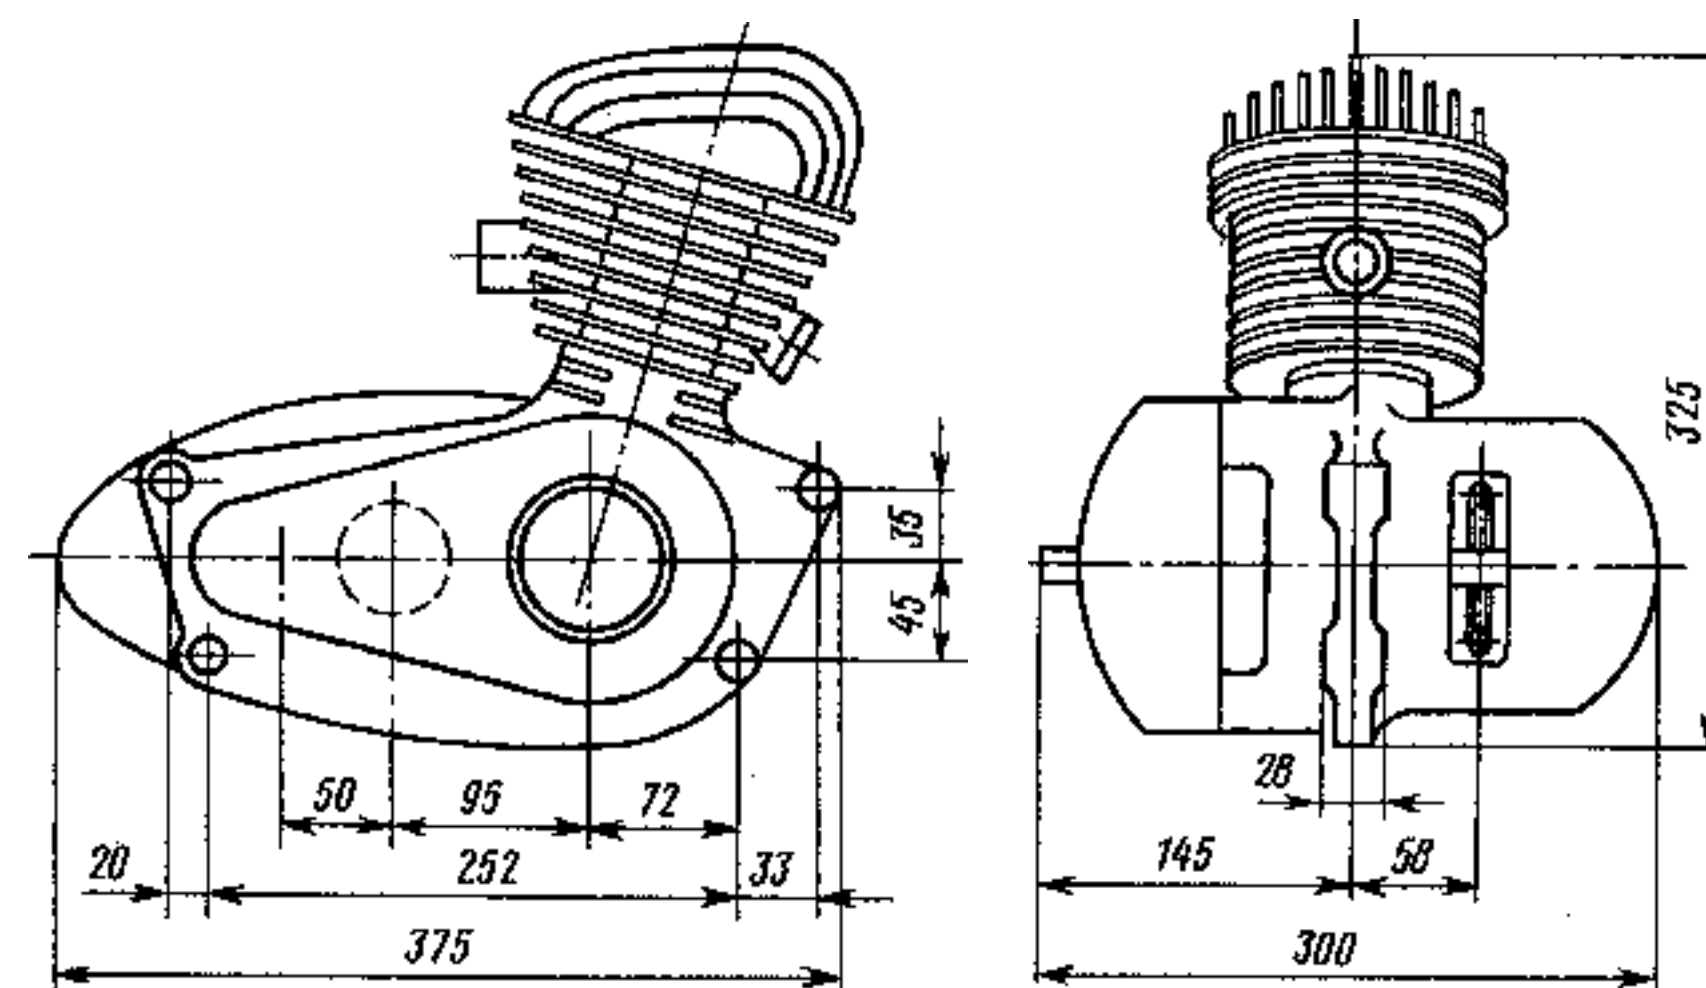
Габариты и точки крепления двигателя М-103 (М-104)
